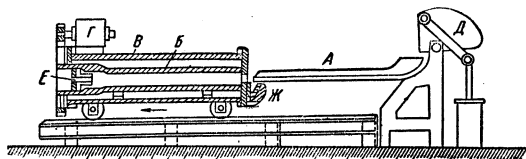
Аппарат де-Лаво для центробежной отливки труб.
